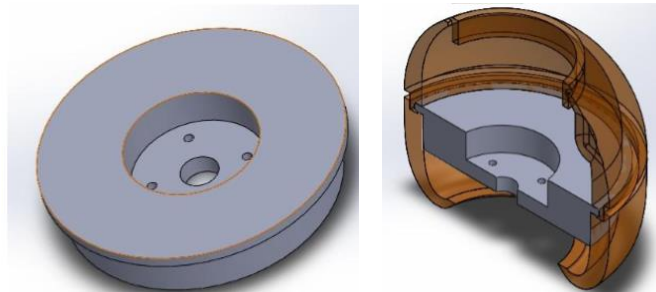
Modelo em SolidWorks do suporte do motor projetado. Adaptado de [76].
